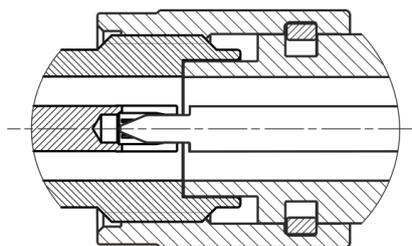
Соединители тип 3,5 мм и IX (розетка слева, вилка справа)
